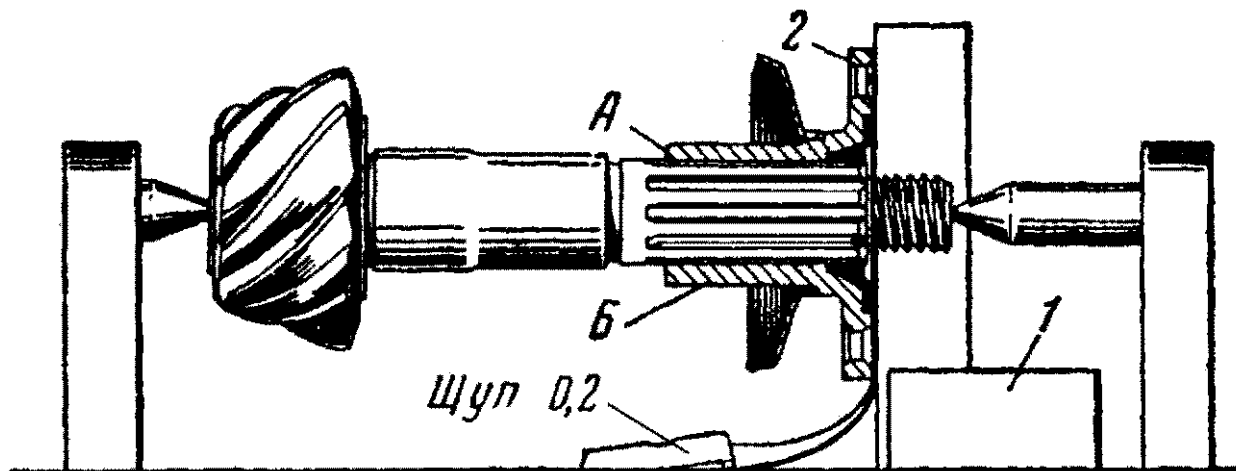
Проверка биения фланца вала ведущей шестерни:
